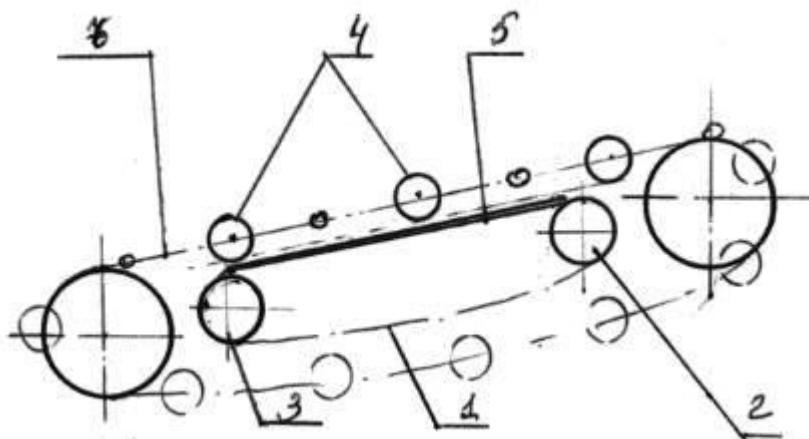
Схема элеватора с вращающимися рамками и приводной цепью:
